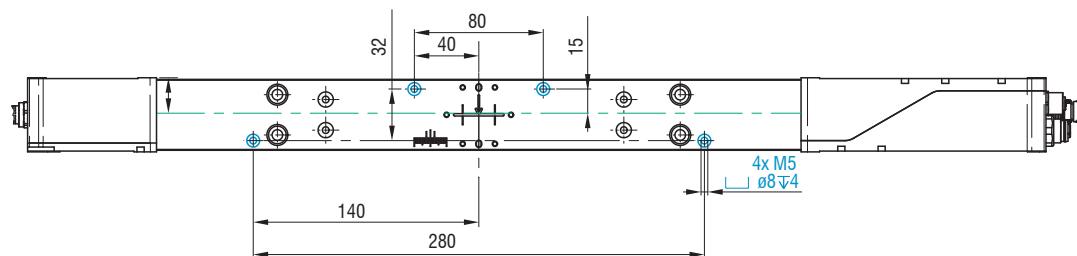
Maßzeichnung Montageschiene ODC2700-40(002), Standardmontage
